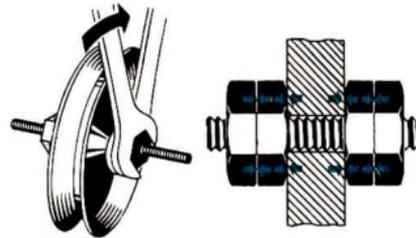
Sicherung der Befestigung durch Gegenmuttern
